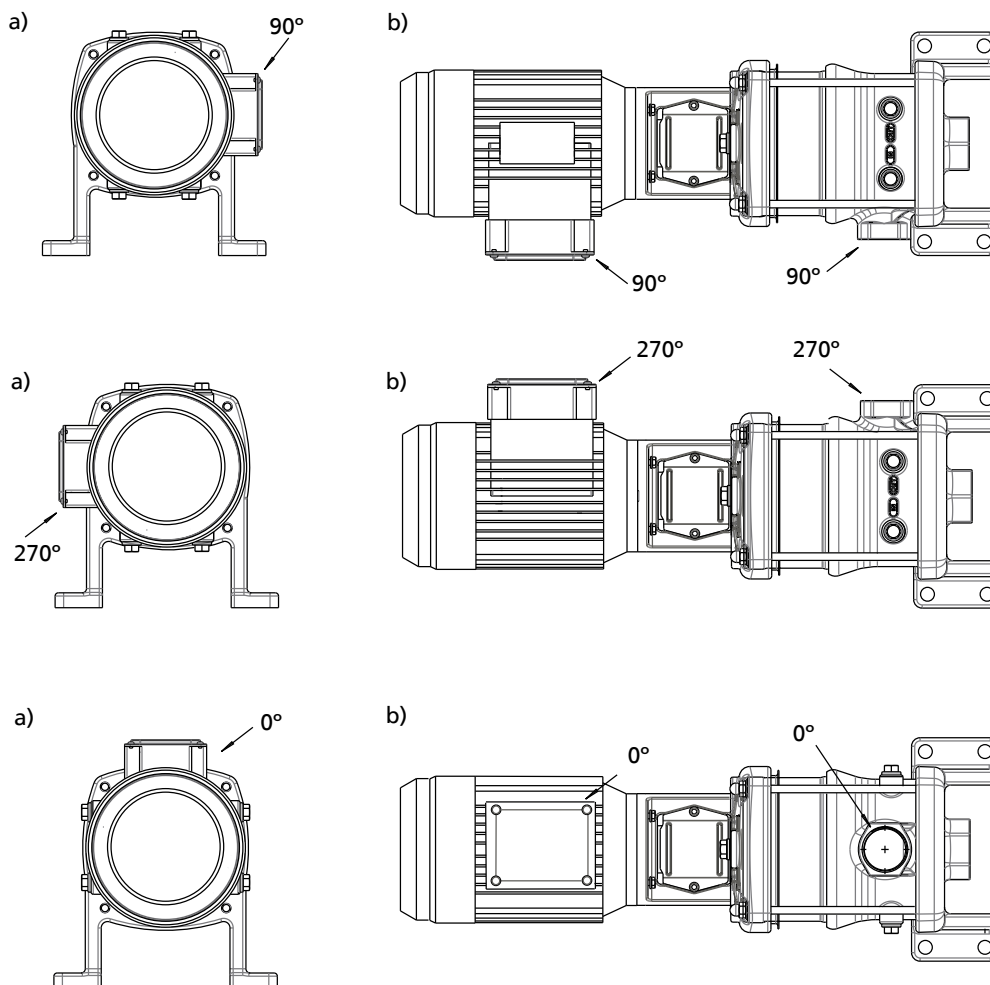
Optionale Aufstellungsarten für Position Klemmenkasten = Position Anschluss Druckseite a) Seitenansicht (vom Motor aus gesehen) b) Draufsicht
